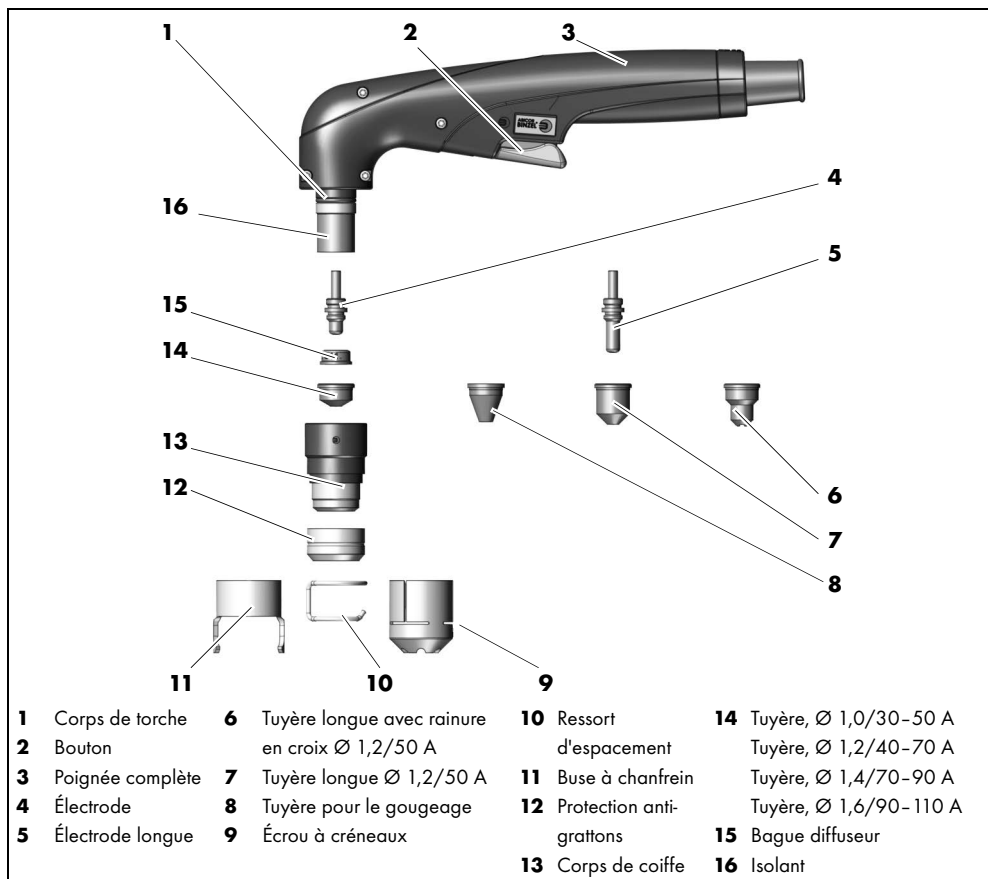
Vue d'ensemble d'ABIPLAS® CUT 111 HF
